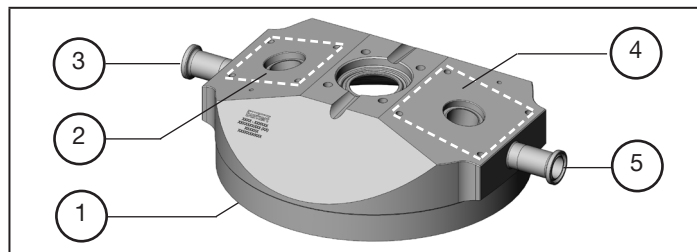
Conexión por soldadura para el cuerpo de válvula en un tanque
